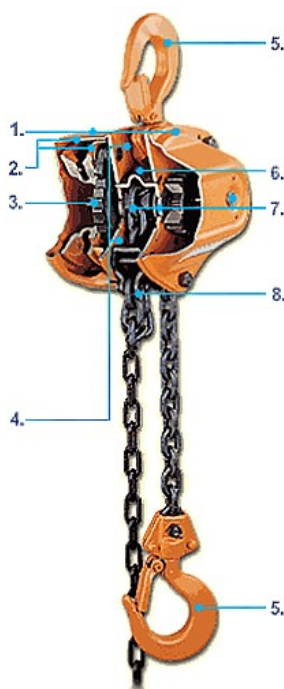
1 - Стальной штампованный корпус; 2 - Двойное защитное покрытие; 3 Тормозной механизм; 4 - Двойные надежные защелки у трещотки; 5 Нижний и верхний крюк; 6 - Направляющие грузовой цепи; 7 - Игольчатый подшипник; 8 - Закрепление конца цепи.
